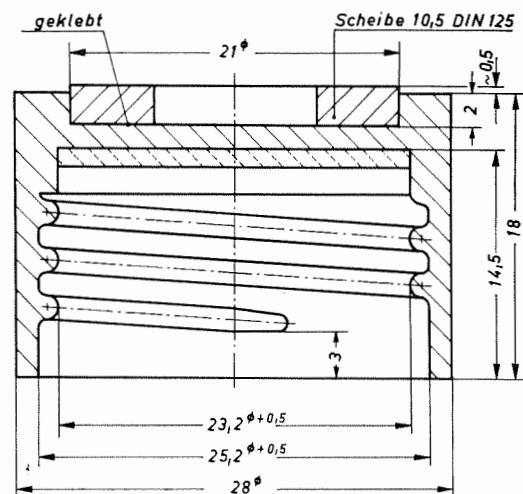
Maßzeichnung von Verschuß und Gewinde der „Normflasche“.
